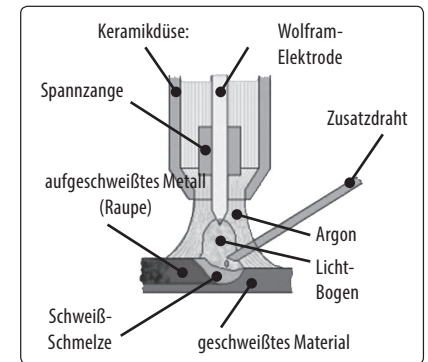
, Prinzip der TIG-Methode mit Einsatz vom Schweißstab
